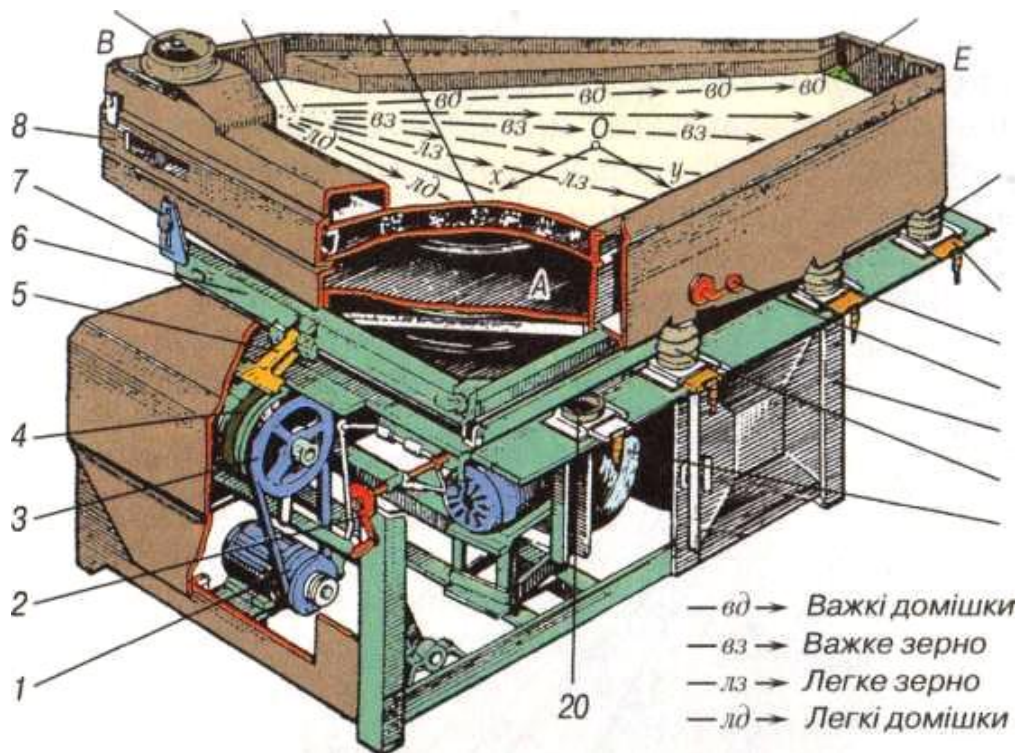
Пневматичний сортувальний стіл ПСС-2.5В: 1 - варіатор; 2 - регулятор; 3 - механізм приводу; 4 - противага; 5 - шатун; 6 - рамка; 7 - кронштейн; 8 - дека; 9 - горловина; 10 - сітка; 11 - повітровирівнювальна решітка; 12 - клапан; 13, 15, 18 і 20 - приймачі; 14 - заслінка; 16 - важіль; 17 - рама; 19 – вентилятор.
